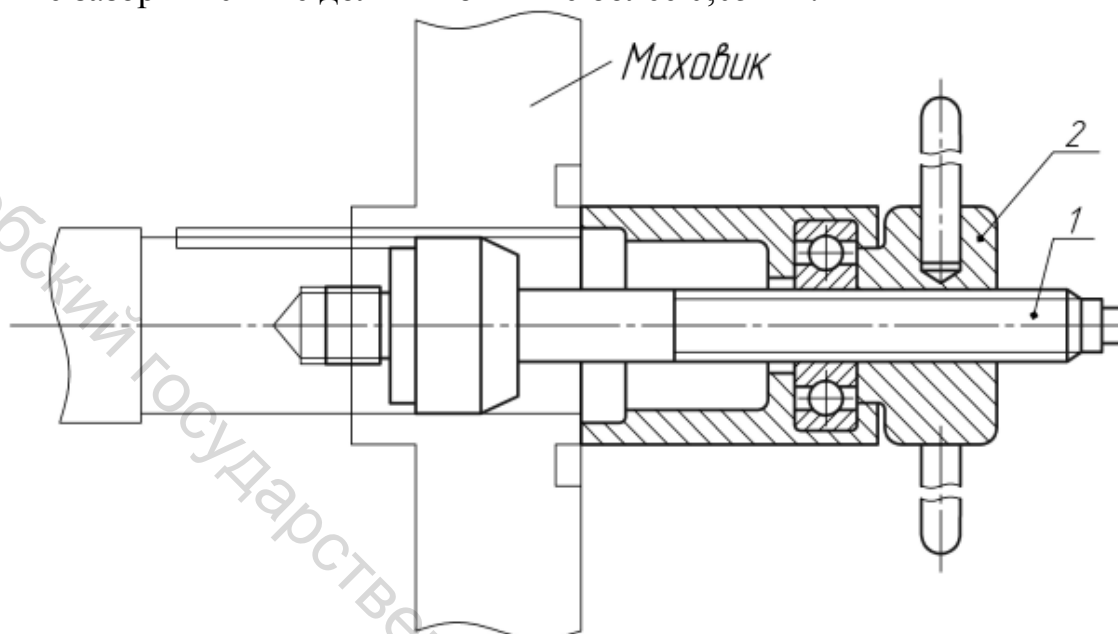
Приспособления для монтажа маховиков и шкивов – винтовое
